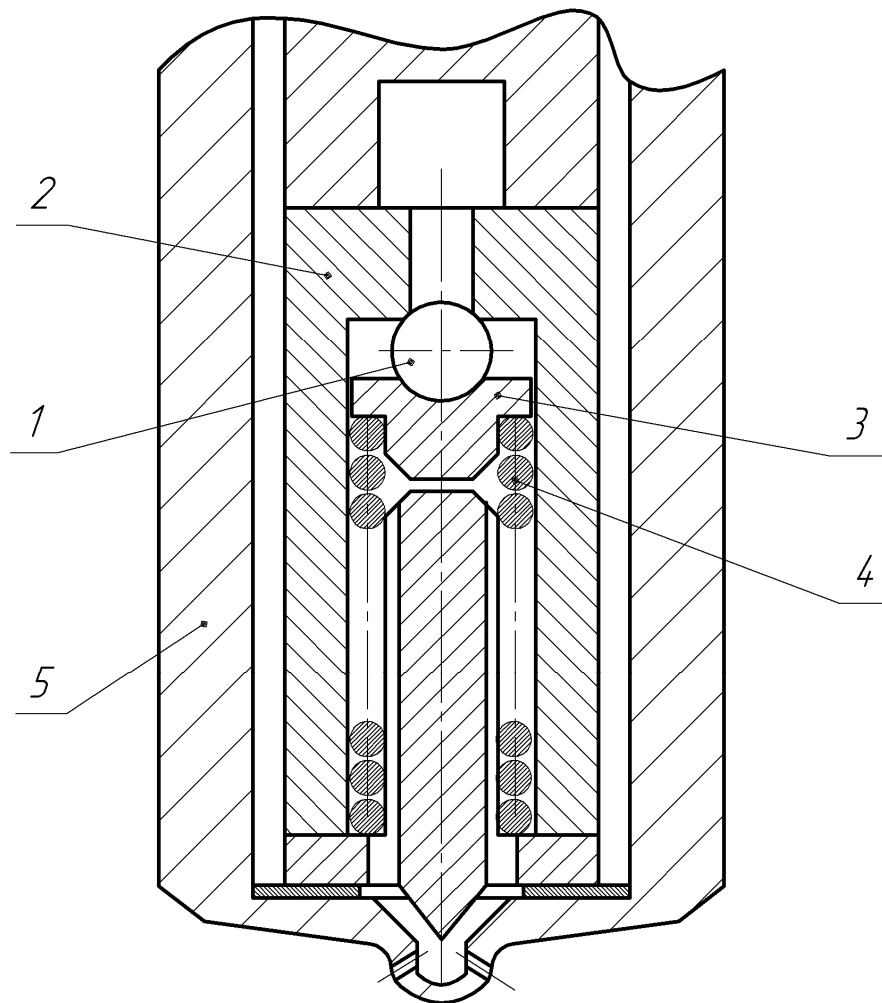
Принципова схема розпилювача форсунки із запірною сферою:
